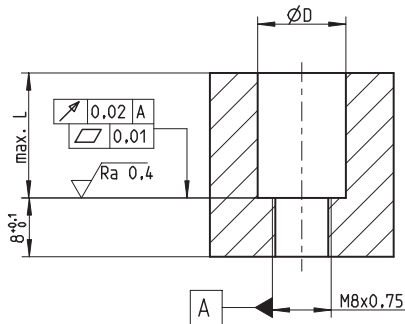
Einbau brennraumbündig. Bohrung ø gemäss Werkzeug, Bild 4 oder Bild 5
